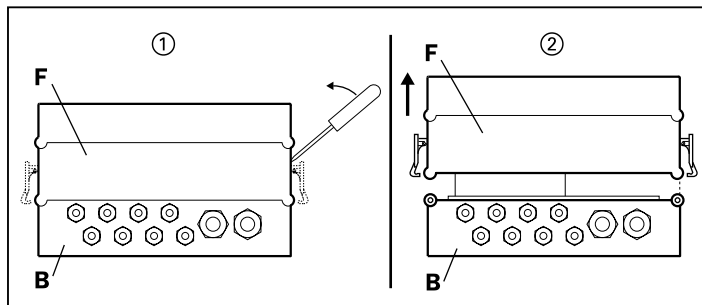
Caixa IP 65, retirar a parte frontal da caixa
